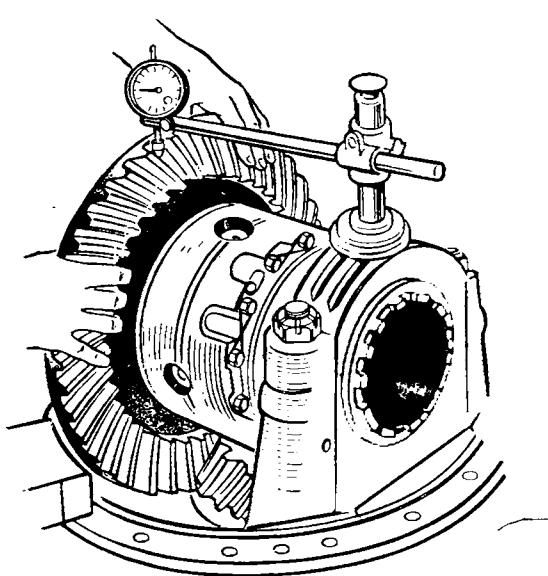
Проверка бокового зазора в зацеплении главной передачи
